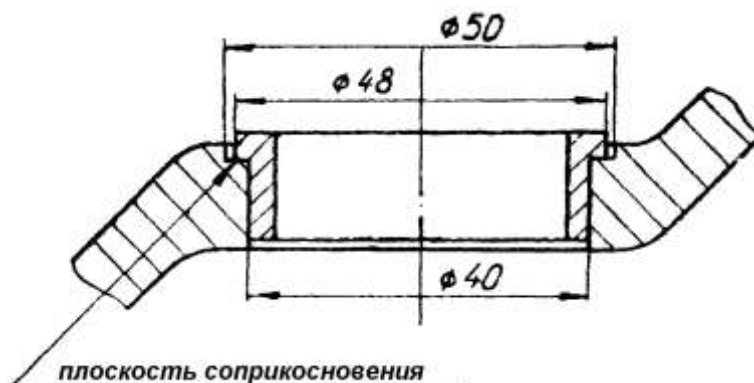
Зазор между цилиндрическими поверхностями $\varnothing 48$ и $\varnothing 50$
